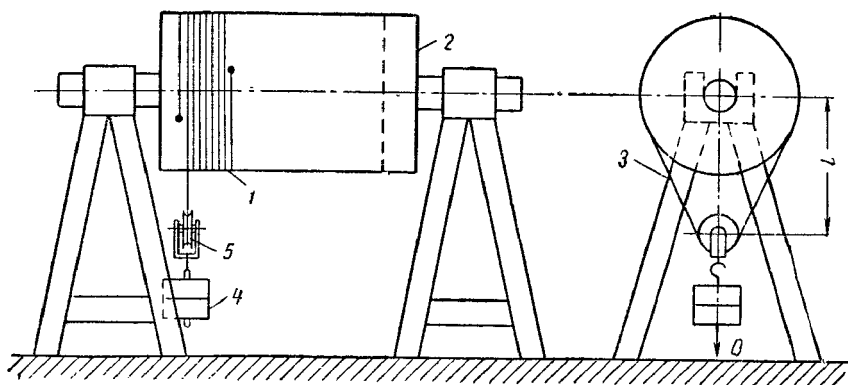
Приспособление для наложения бандаж роторов и якорей:
